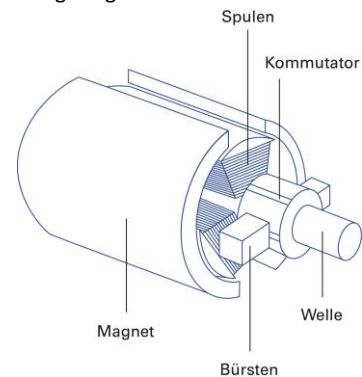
Aufbau eines DC-Motors mit Stator magnet, Rotorwicklungen, Kommutator, Bürsten und Motorwelle.
